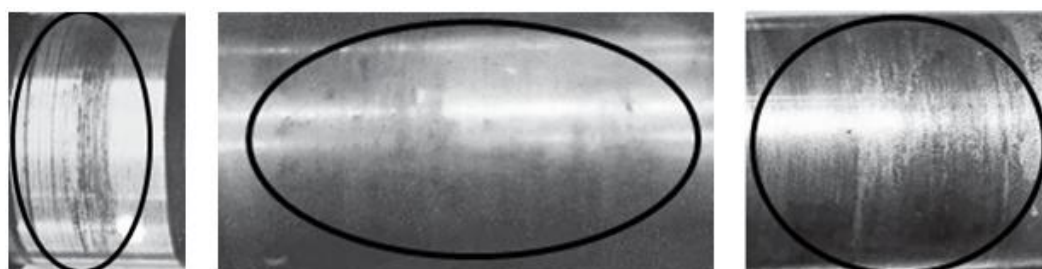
Внешний вид посадочных поверхностей валов, подвергшихся износу
